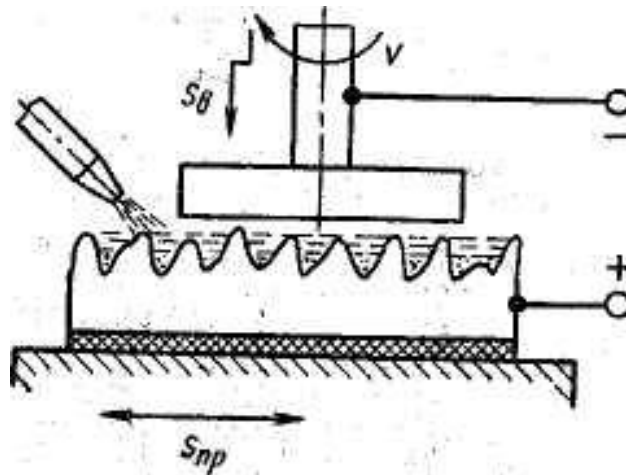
Схема анодно-механічної обробки плоскої поверхні
